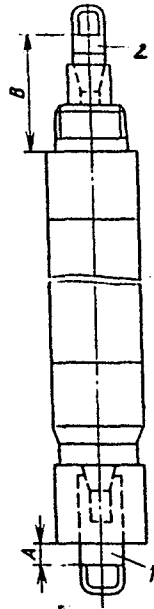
Контроль регулировки турбинных секций с унифицированными присоединительными размерами (при нижнем положении вала):
